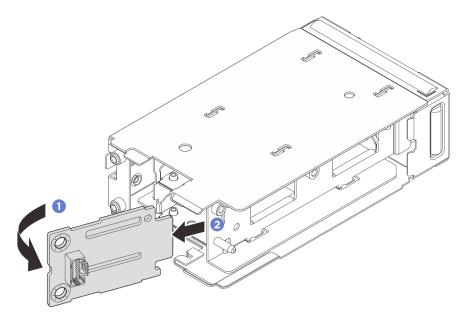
Extracción de la placa posterior de arranque M.2 frontal
